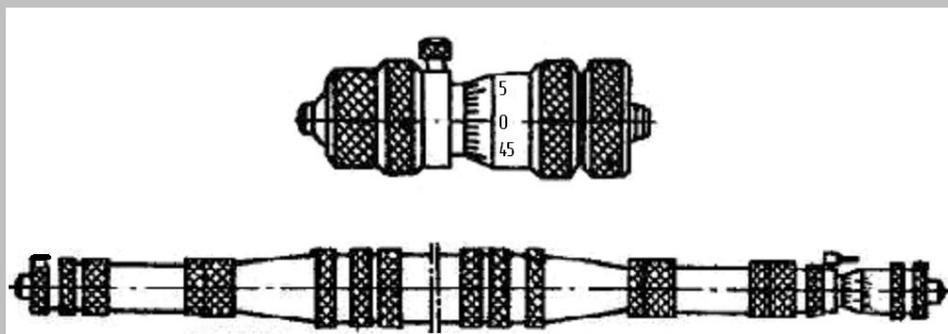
микрометрический нутромер. Нутромер с удлинителями. Цена деления шкалы барабана 0,01 мм. Пределы показаний (микрометрической головки) — 50—63 и 75—88 мм; пределы измерений нутромеров: 50—150, 50—400, 50—900, 50—1500, 75—175, 75—575, 150—1200, 150—4000 мм, 500—10000 мм.
